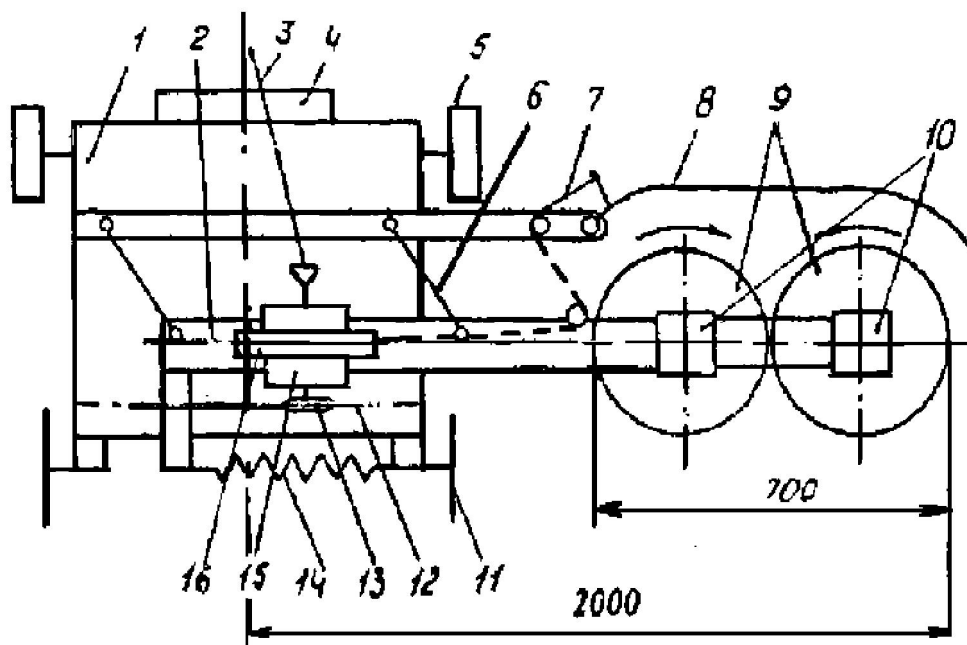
Конструктивна схема фрези: 1- рама; 2 - висувна секція; 3 - карданна передача; 4 - автозчеплення; 5 - опорно-регулюючі колеса; 6 - паралелограмний механізм; 7 - трос; 8 - щуп; 9 - фрезерні ротори; 10 - конічні редуктори; 11 - дисковий ніж; 12 - ланцюг; 13 - зірочка; 14 - зворотна пружина; 15 - редуктор; 16 - фрикційна муфта
